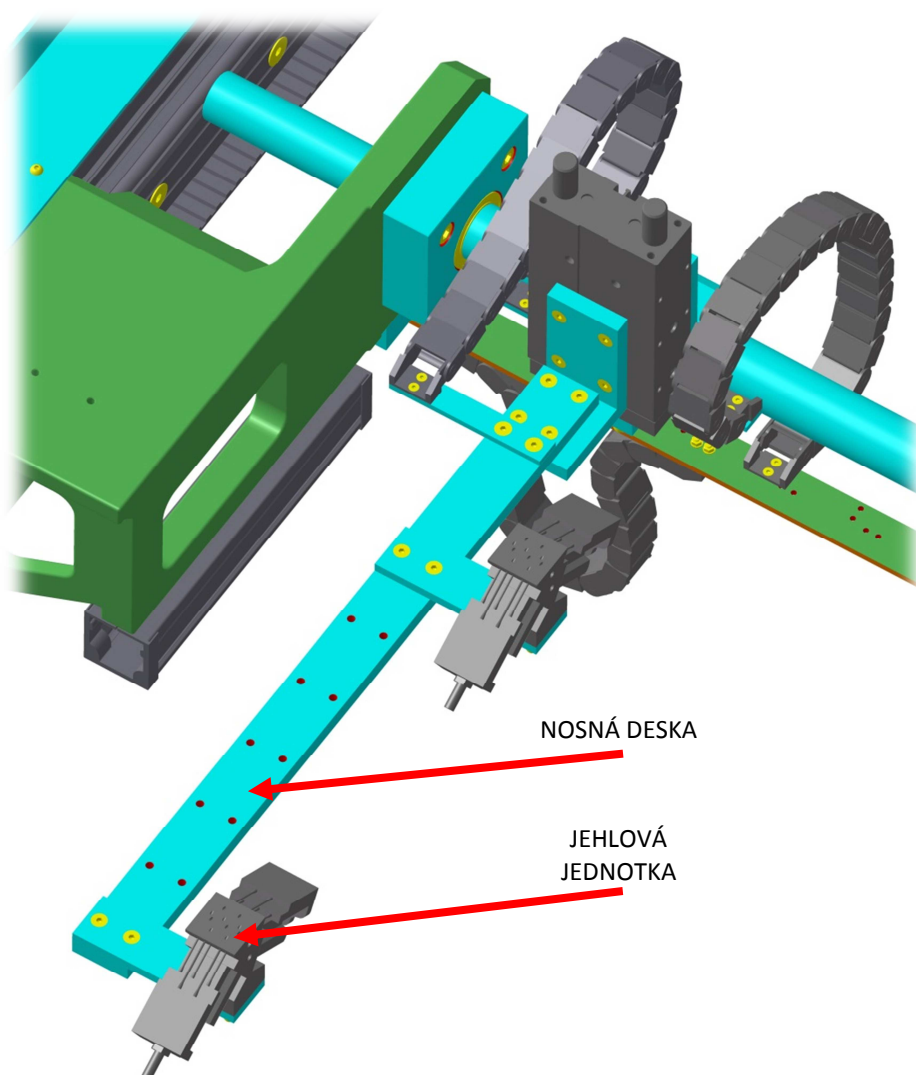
Pravá strana úchopu podávacího ústrojí - varianta I
